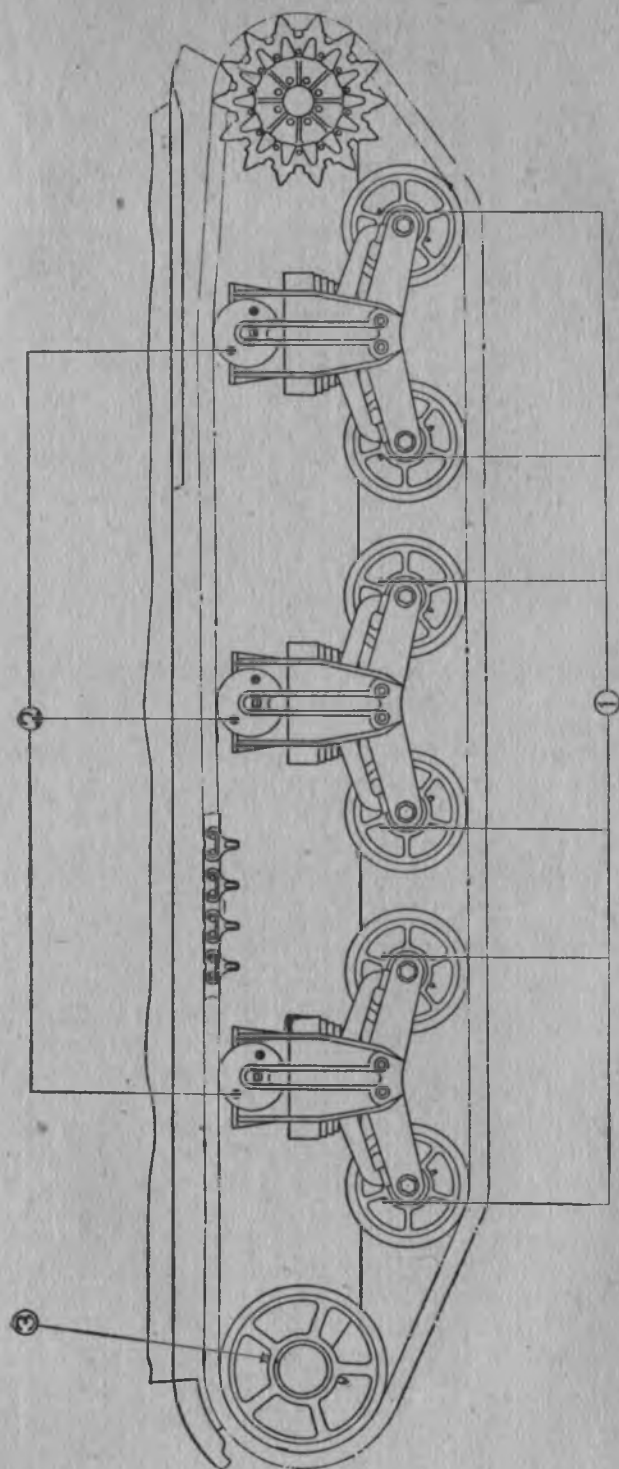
Ходовая часть танка с указанием точек смазки:
